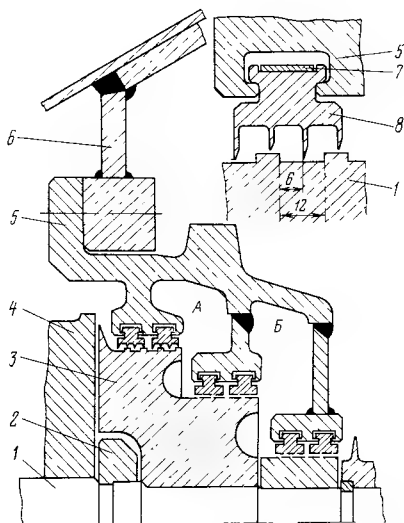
Уплотнение ЦНД мощной турбины: 1 — ротор; 2 — стопорное кольцо; 3 — втулка уплотнения; 4 — диск последней ступени; 5 — обойма уплотнения; 6 — фланец крепления обоймы; 7 — плоская пружина; 8 — сегмент уплотнения
